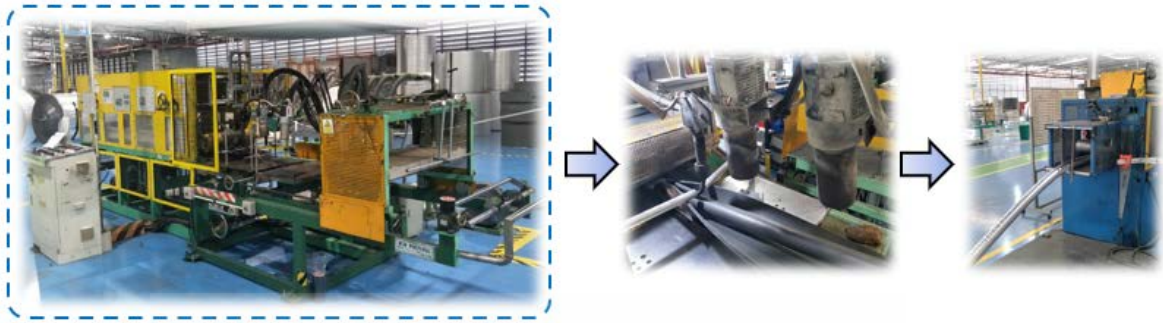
ลักษณะของเครื่องกรีดม้วนโฟม (Slit machine)
